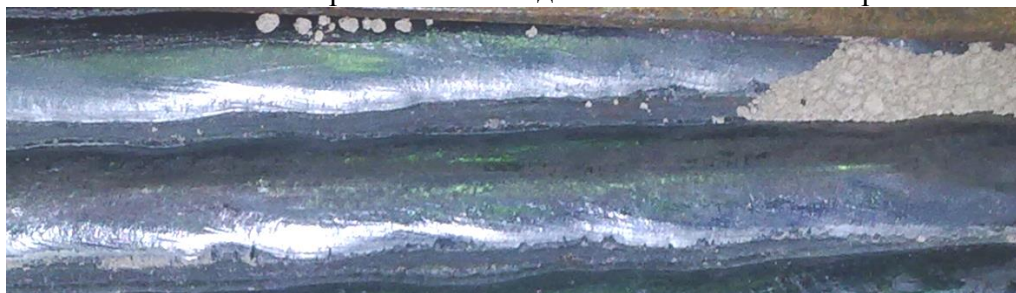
Внешний вид валиков, наплавленных под флюсом опытных партий 11 и 12
